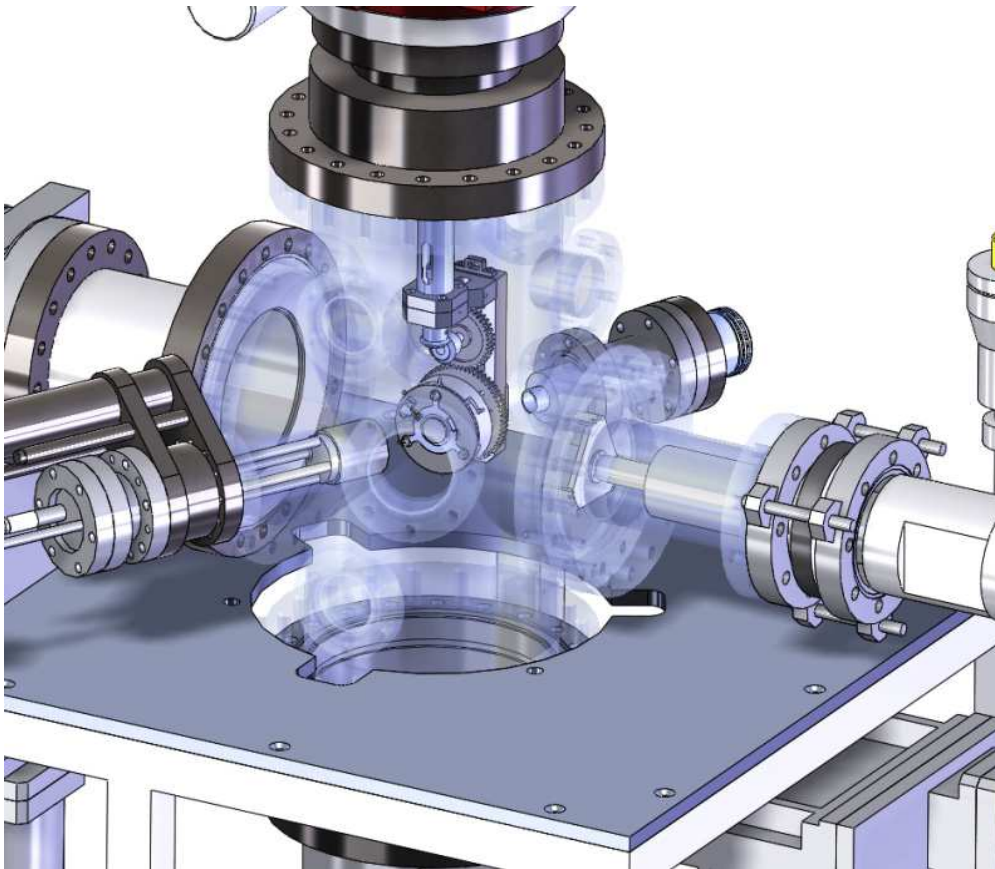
Configuration expérimentale de la chambre de préparation de surfaces.
